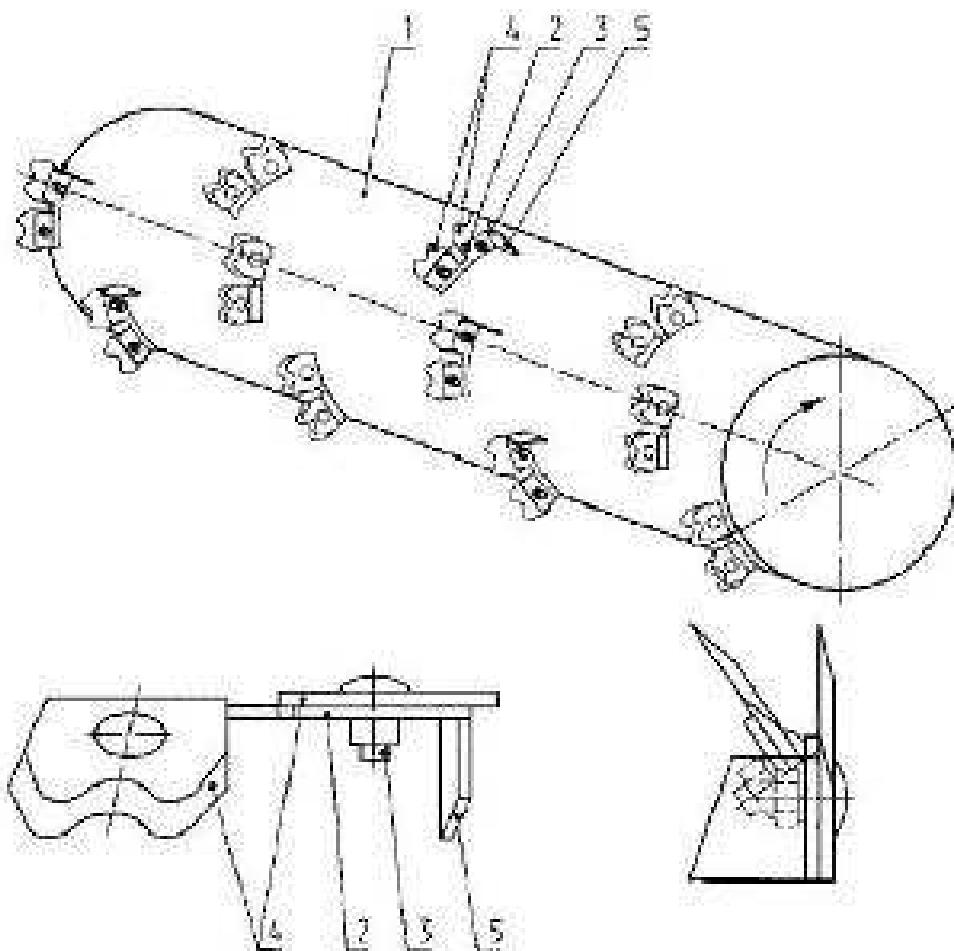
Устройство фрезерного типа для отцепления и подачи стебельчатых кормов
